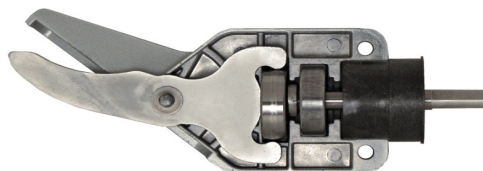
Angrenaj capete modulare (Varianta electrică 14.4 v/220v).
